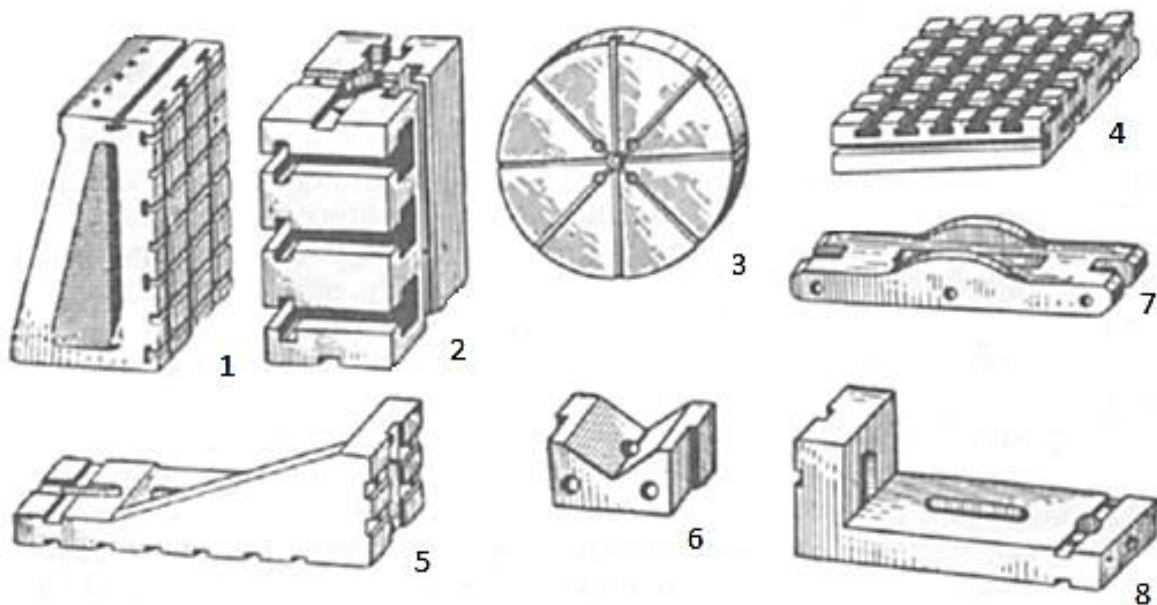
Стандартизованные детали универсально-сборных приспособлений:
